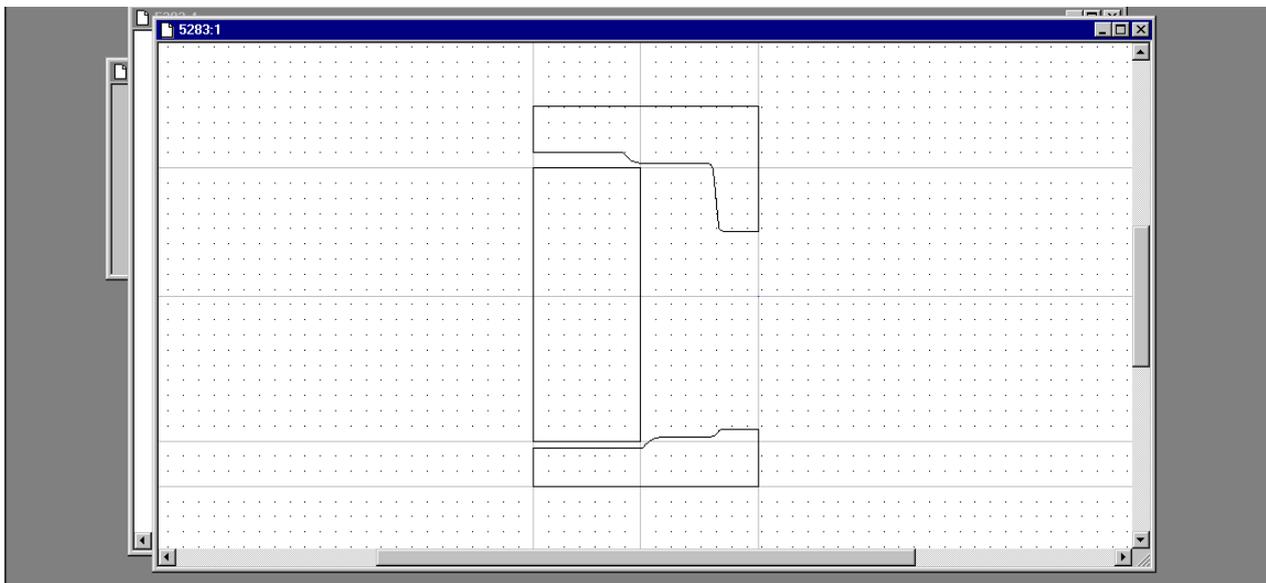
Чертеж с заготовкой и штамповыми блоками
